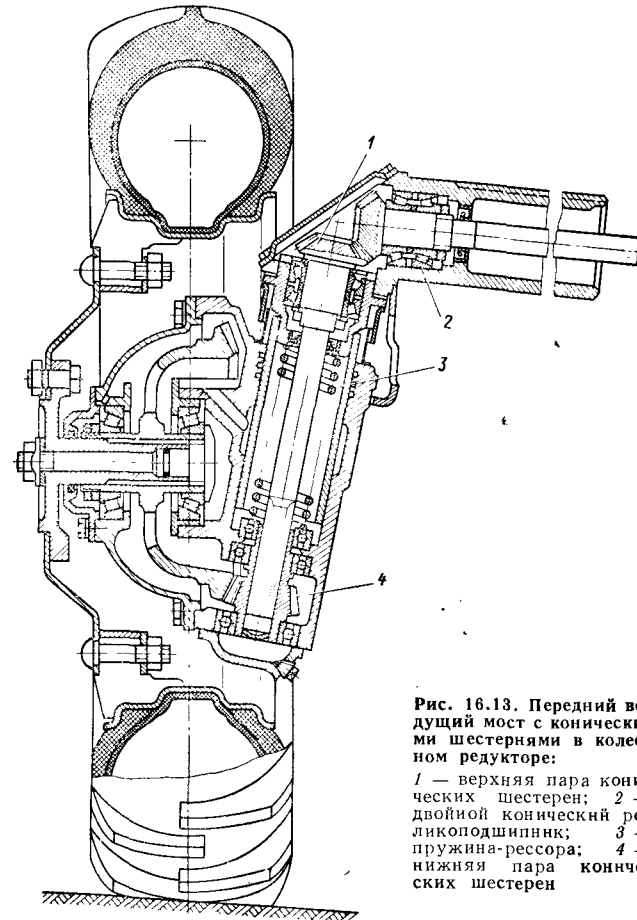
Передний ведущий мост с коническими шестернями в колесном редукторе:
